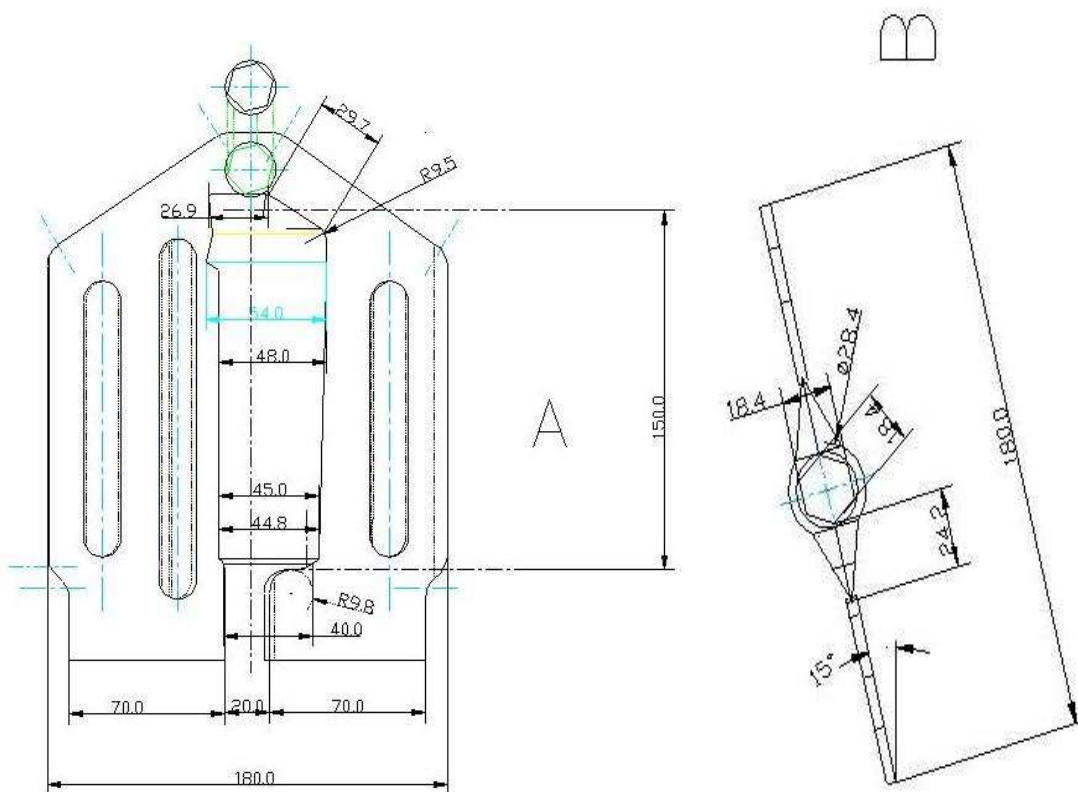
Planta do impelidor utilizado no AnSBR. A. Corte transversal da peça. B. Vista superior da peça (medida em mm).
